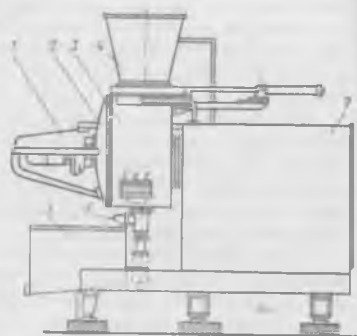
Вакуум-варочная установка «Комби-Кут»:
